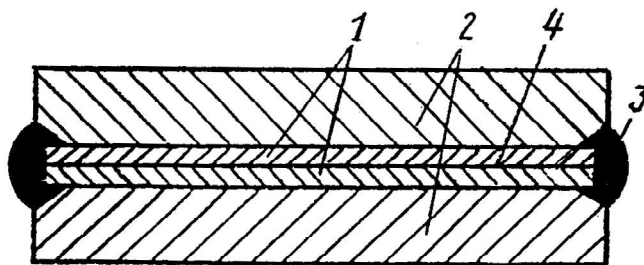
Схема чотиришарового симетричного пакета, що є заготовкою для виготовлення двошарових листів: 1 – пластини корозійностійкої сталі; 2 – пластини основного шару; 3 – зварний шов; 4 – поверхня контакту пластин з корозійностійкої сталі
